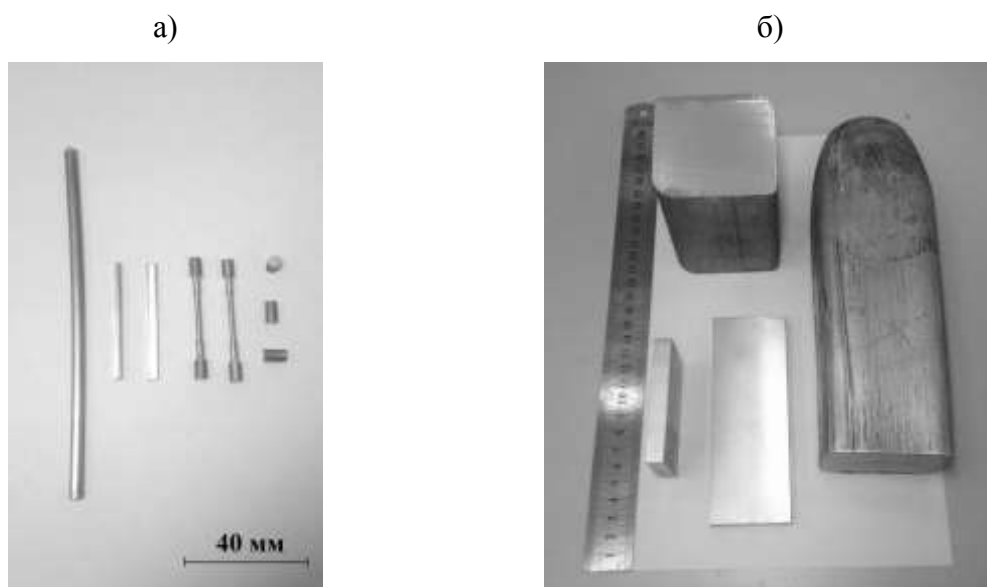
Общий вид экструдированных заготовок и изготовленных из них образцов
